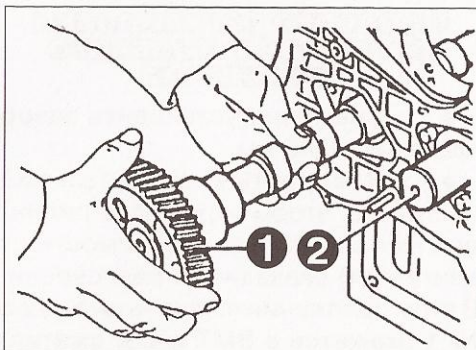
Установка распределительного вала в картер блока цилиндров.
